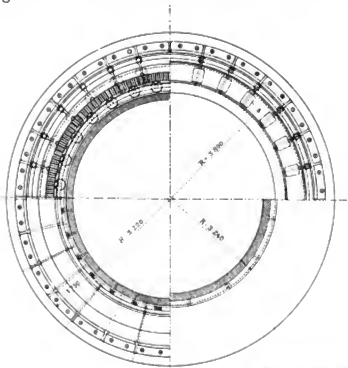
GRUNDRISSE DES ROLLENKRANZES
